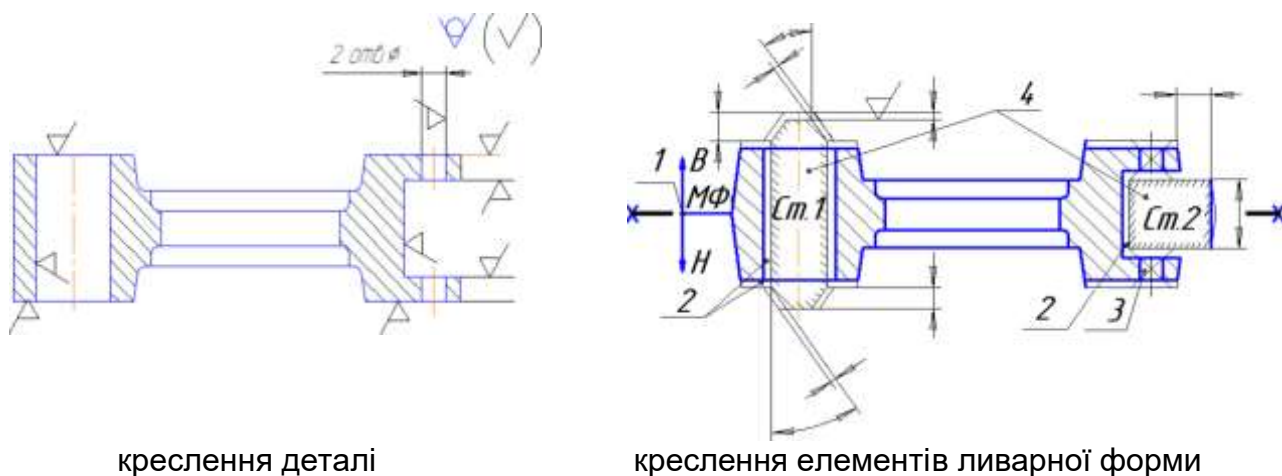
Розробка технологічно-ливарних вказівок (елементів ливарної форми)
